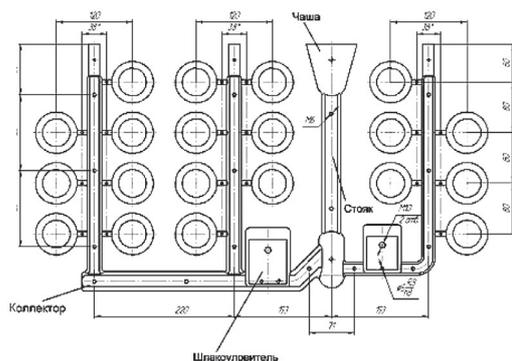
Отливка «Втулка распределительного вала 240-1002067-А» с литниковой системой
